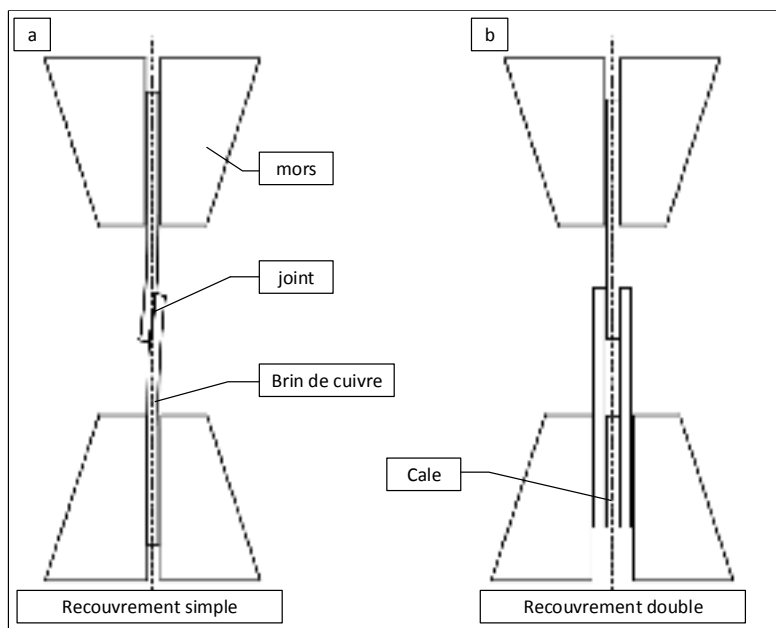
Schéma d'un montage de traction montrant l'impact du type de recouvrement sur le pivotement du joint
